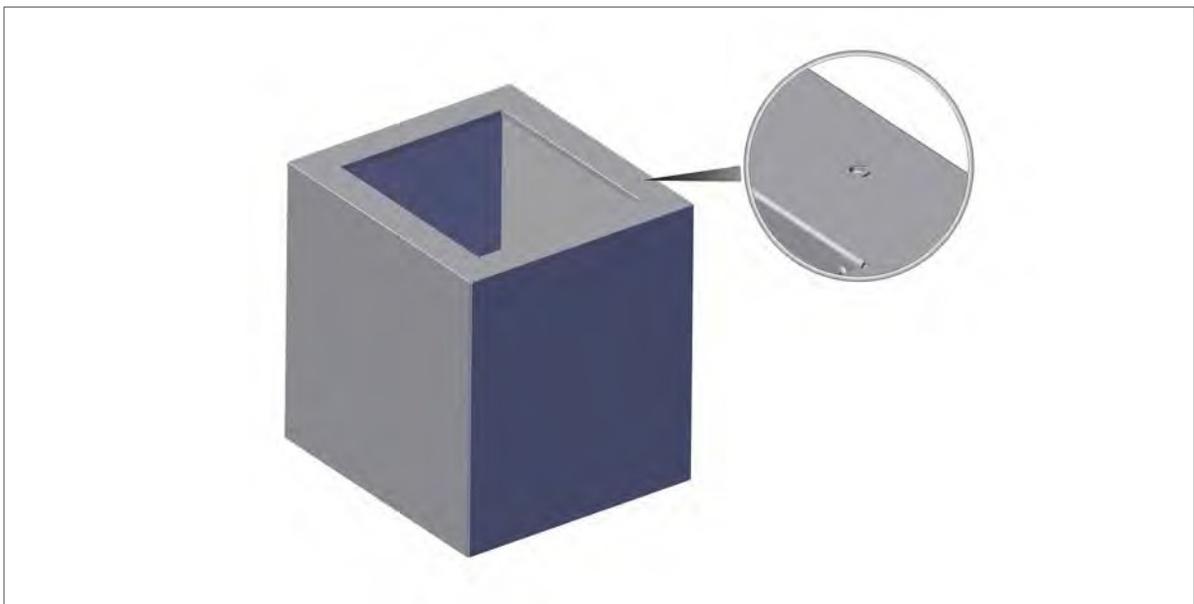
Regard en aluminium; zoom sur un rivet à tige filetée
